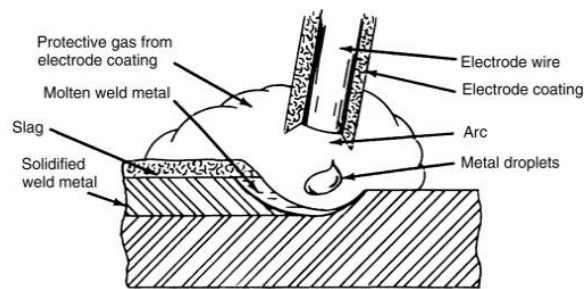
Processo de soldadura por eletrodo revestido [27]
